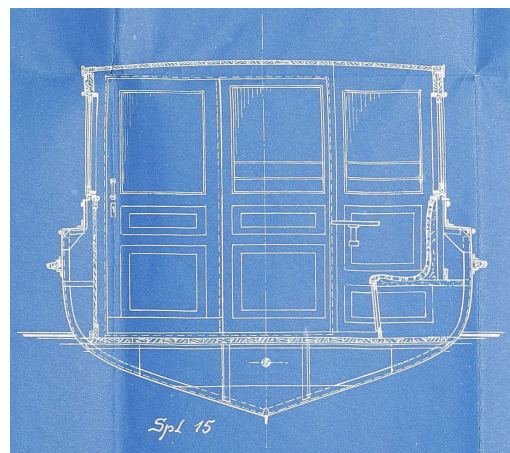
Bauplan „Stadt Emmerich“ 1914.
